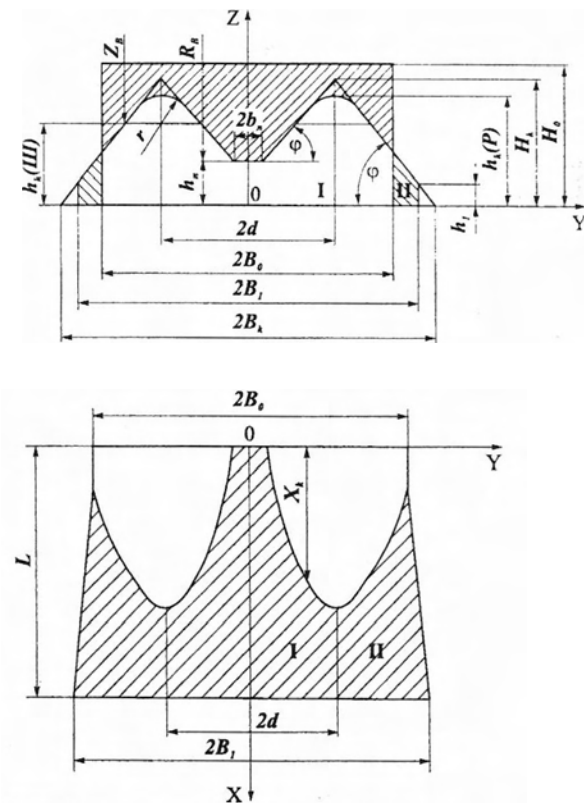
Схема очага деформации при прокатке прямоугольной заготовки в двухручьевых калибрах с ромбической (Р) и шестиугольной (Ш) формой ручьев.
